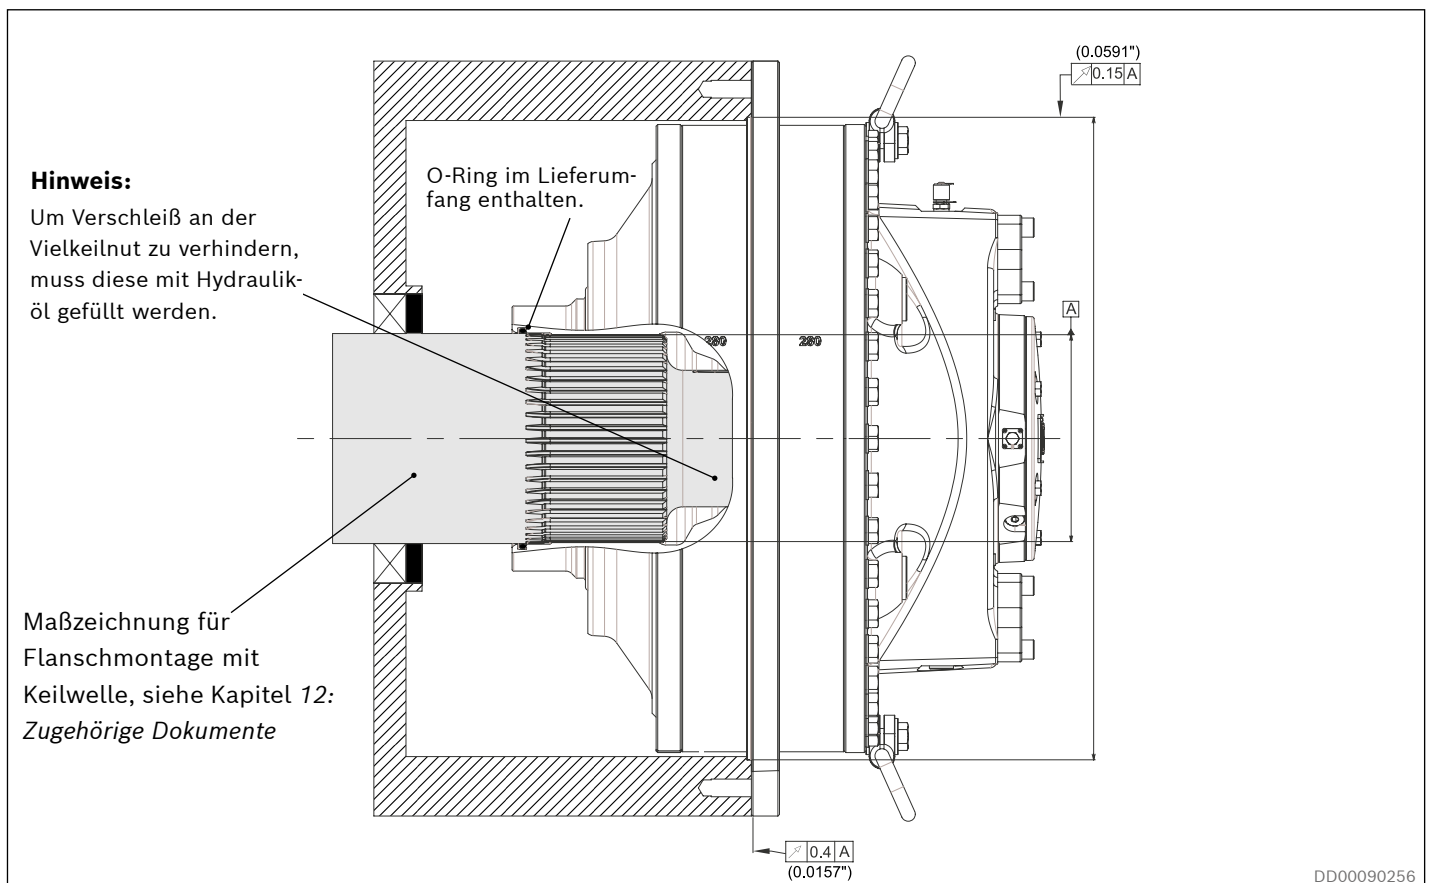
Flanschmontage für CB 280 bis CB 1120.
